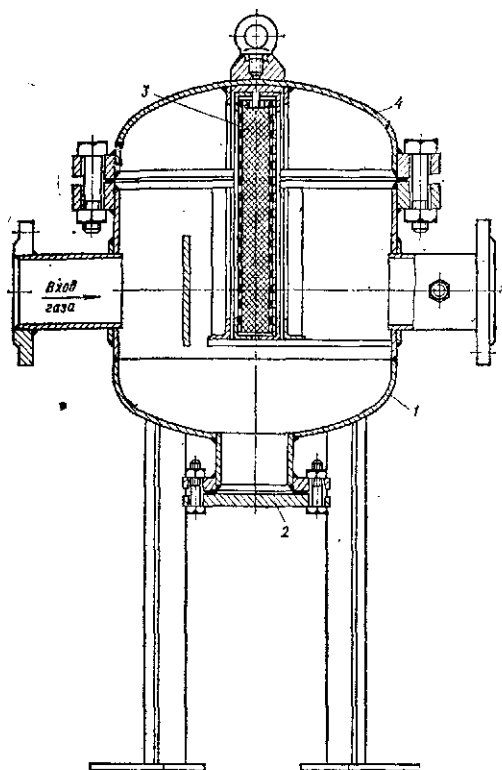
Волосяные стальные сварные фильтры
